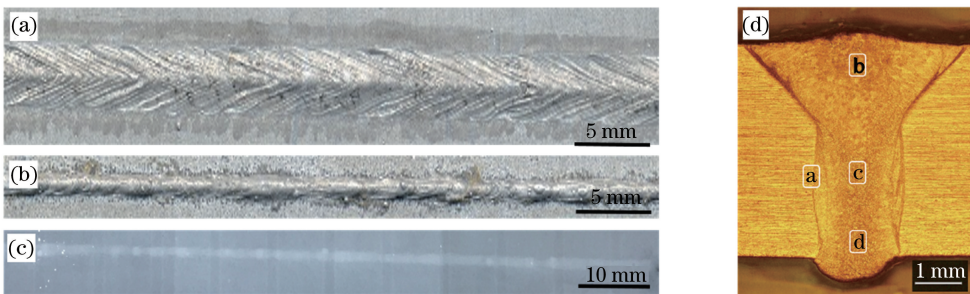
优化参数条件下的焊缝形貌。(a) 焊缝正面; (b) 焊缝背面; (c) X 光探伤底片; (d) 焊缝横截面
